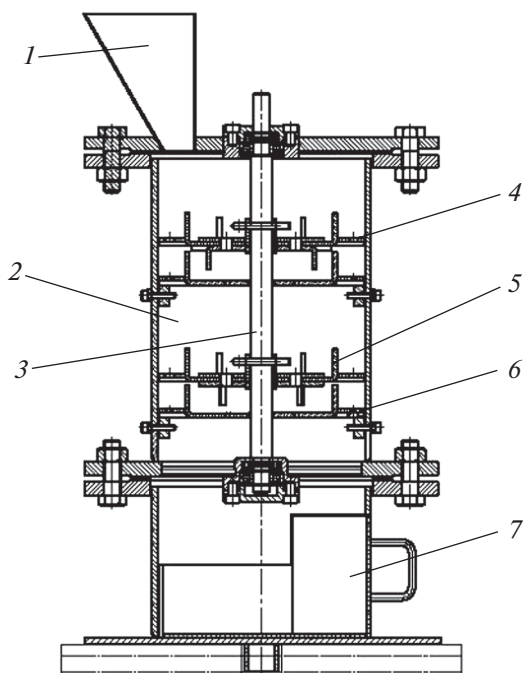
Общий вид измельчителя: 1 – бункер; 2 – цилиндрический корпус; 3 – вал с закрепленными на нем двумя парами измельчающих дисков – верхней 4 и нижней 5; 6 – ножи; 7 – приемный бункер.
